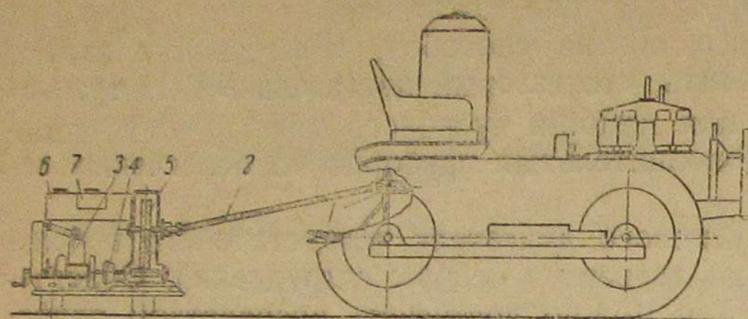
Монтажная схема установки проф. Беляничкова для запуска двигателей тракторов ЧТЗ:
